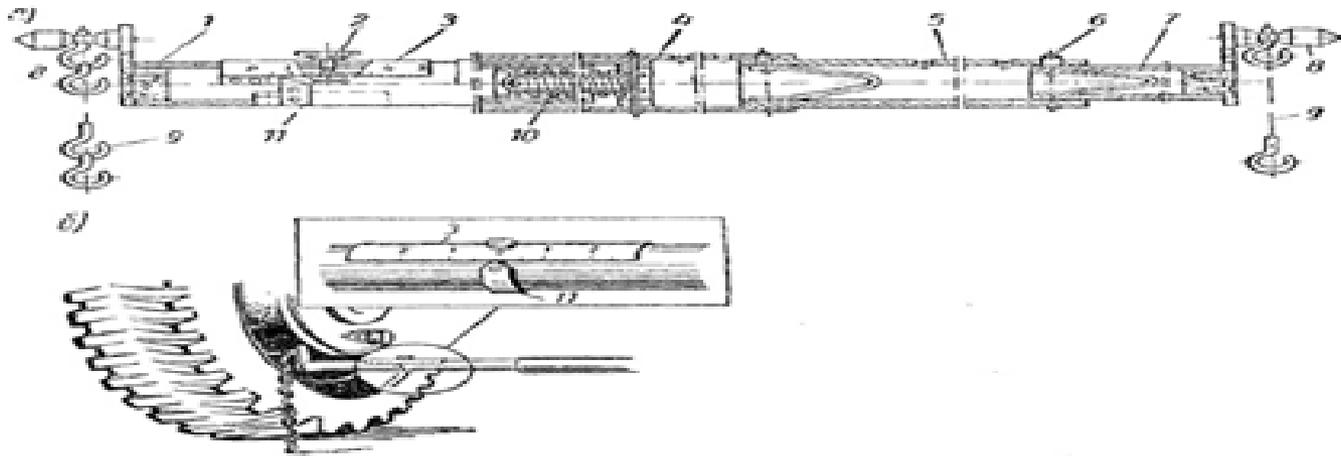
Линейка для проверки углов схождения передних колес автомобиля:
